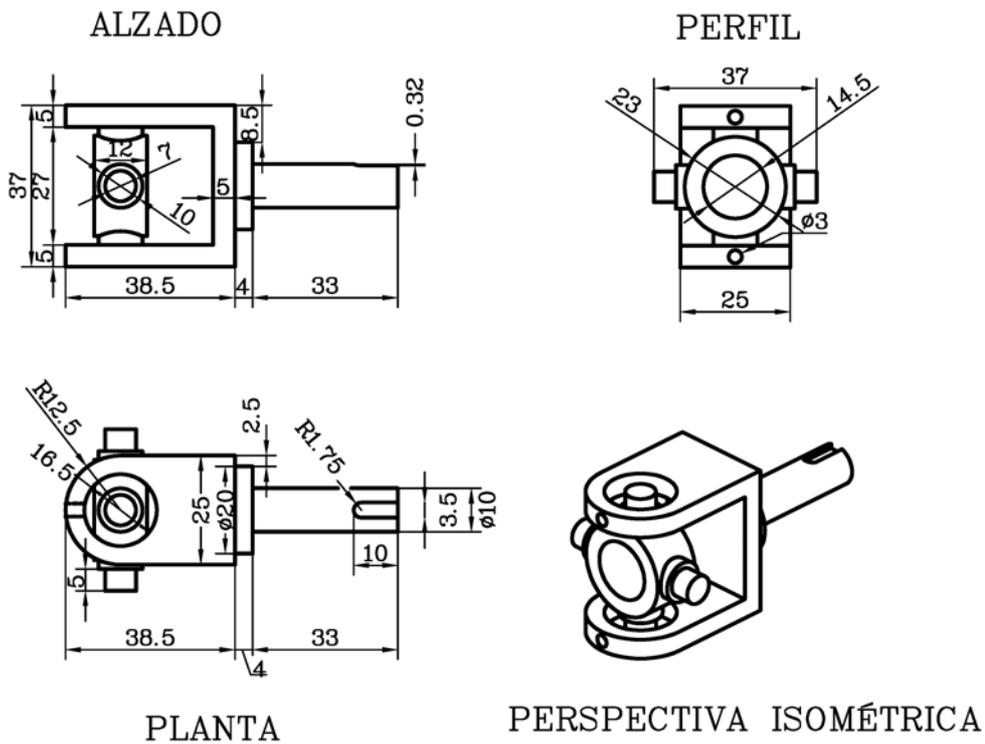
Acotación completa de un mecanismo de maquinaria.
